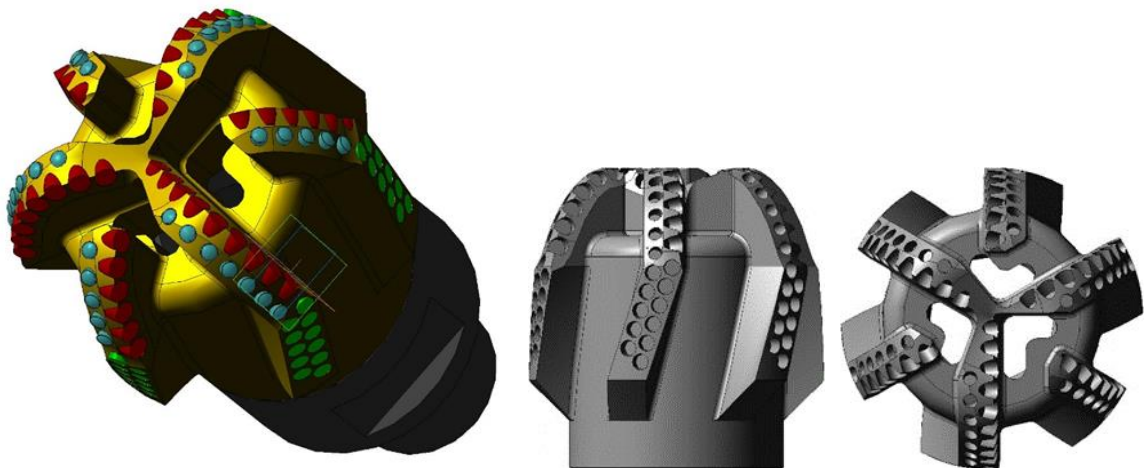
Трехвмірна модель лопатевого суцільнофрезерованого долота ІНМ АП 215,9 С 613 та його корпус (вид спереду і зверху)
